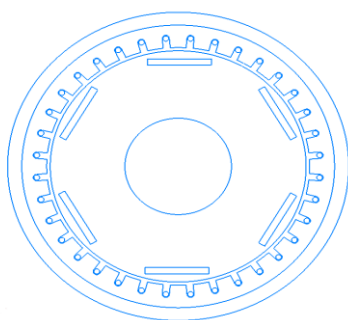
Примерный общий вид синхронного двигателя с неодимовыми магнитами
